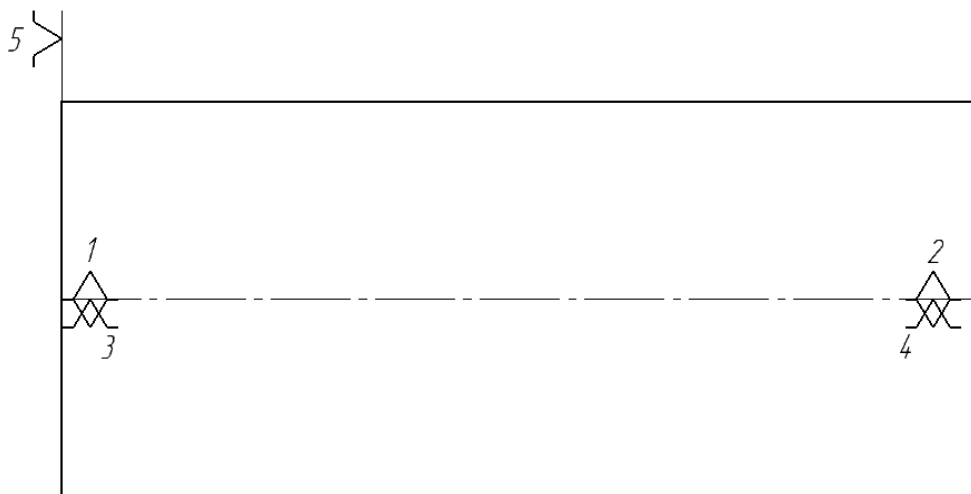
Теоретична схема базування деталі «Вал-шестерня»
